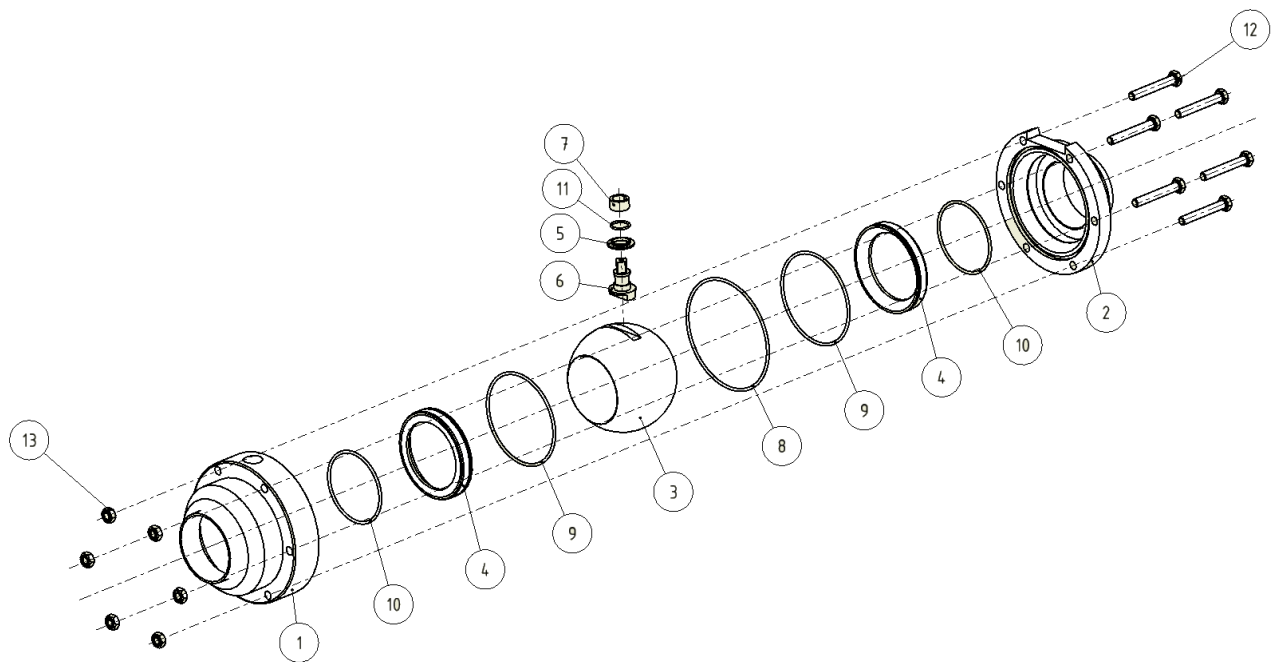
Kugelventil-SS ohne Betätigung (Explosionsdarstellung)
